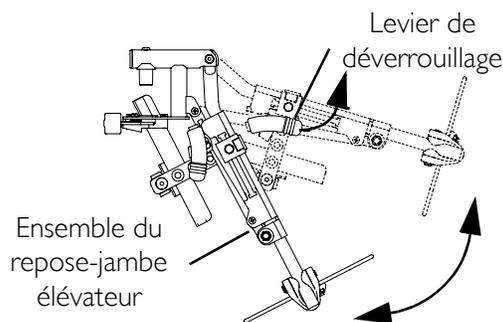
Montée et descente des repose-jambes réglables en hauteur
